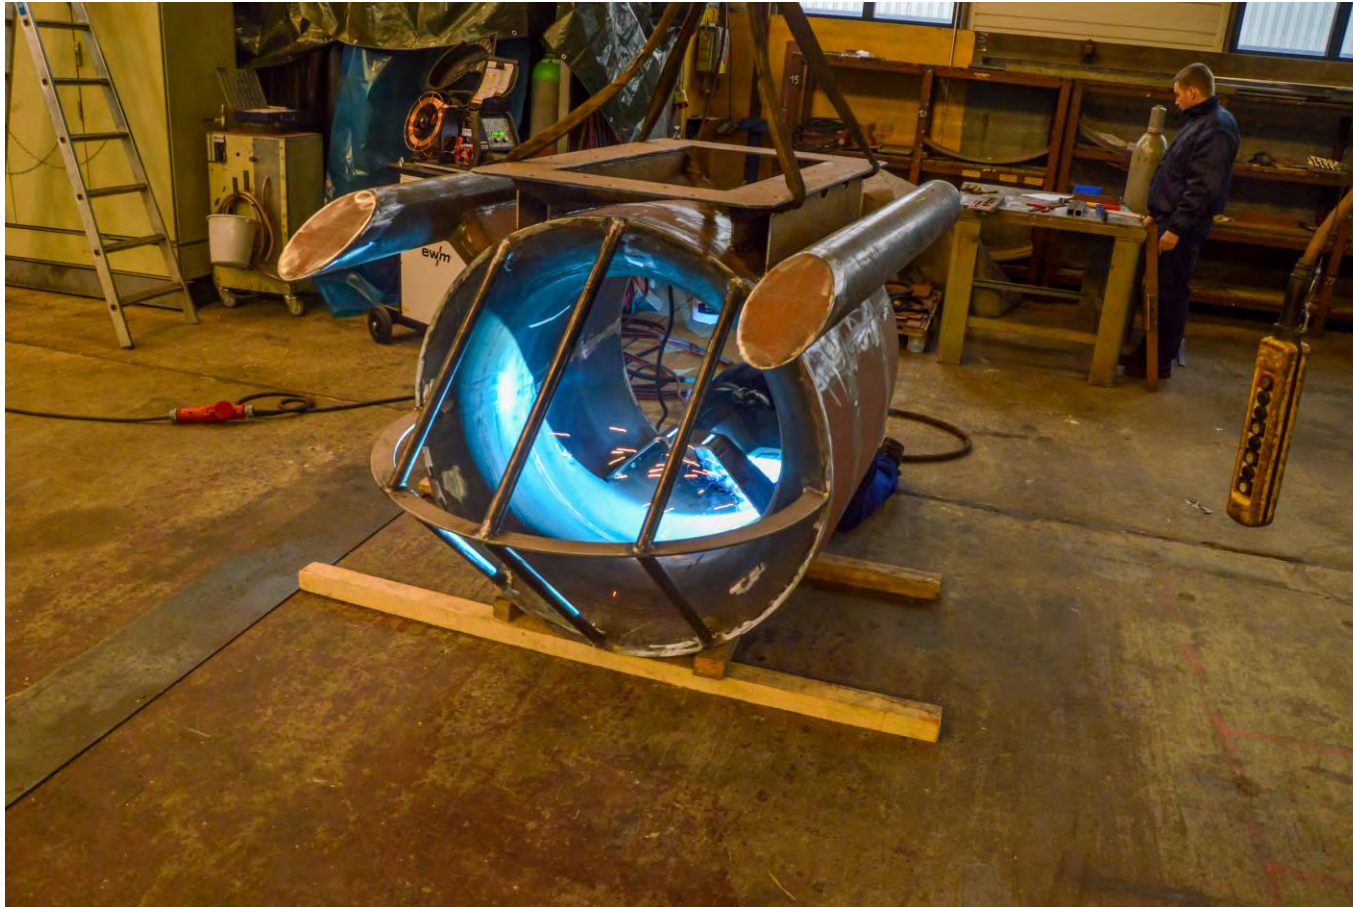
Schweißmontage Generatorhalterung
